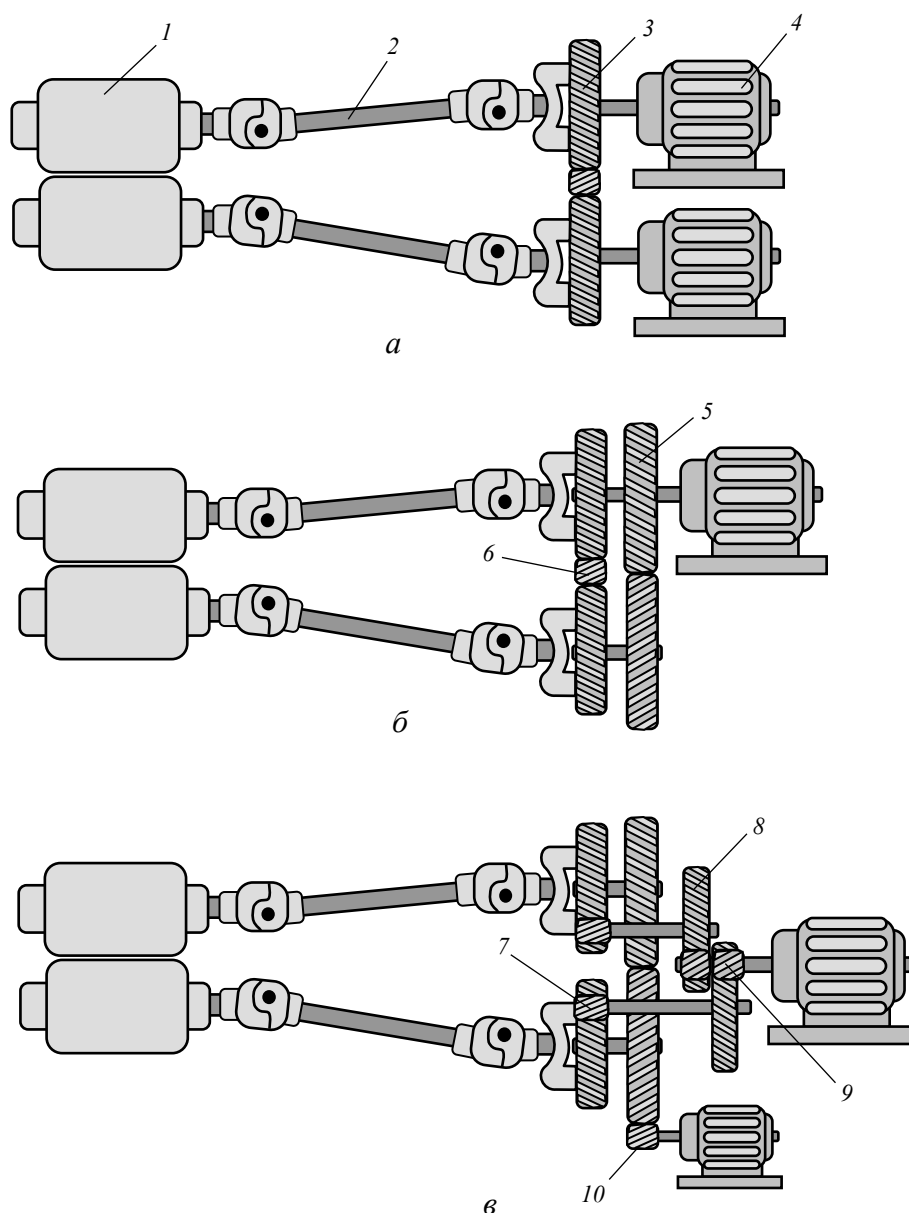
Електроприводи: *а* — адаптивний індивідуальний; *б* — адаптивний груповий; *в* — рекуперативний (*1* — робочий валок; *2* — шпиндель; *3* — диференціал; *4* — електродвигун; *5* — шестерений валок; *6* — балансірна шестерня; *7, 8, 9, 10* — шестерні і зубчасті колеса балансірної ланки)
